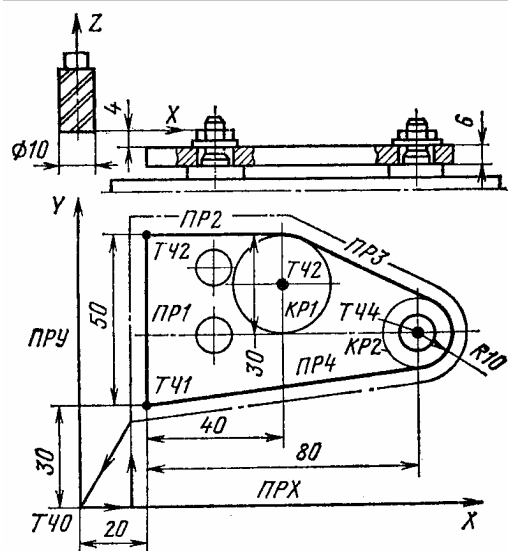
Схема обработки заготовки (к заданию 16.14)
